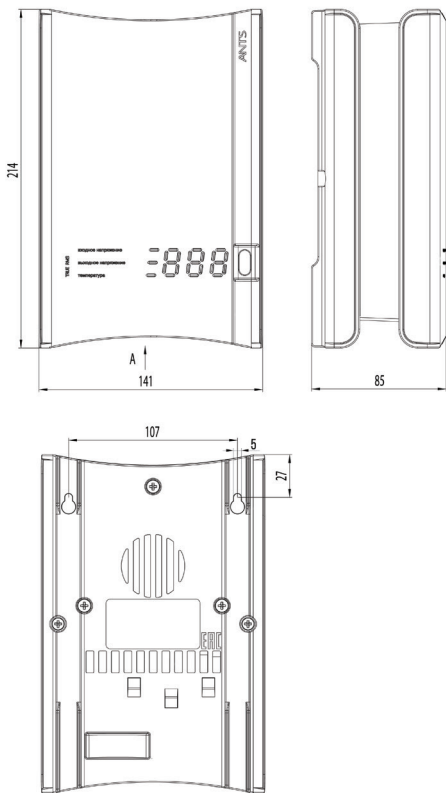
Габаритные и установочные размеры стабилизаторов КилоГерц 1-3 и 1-5
